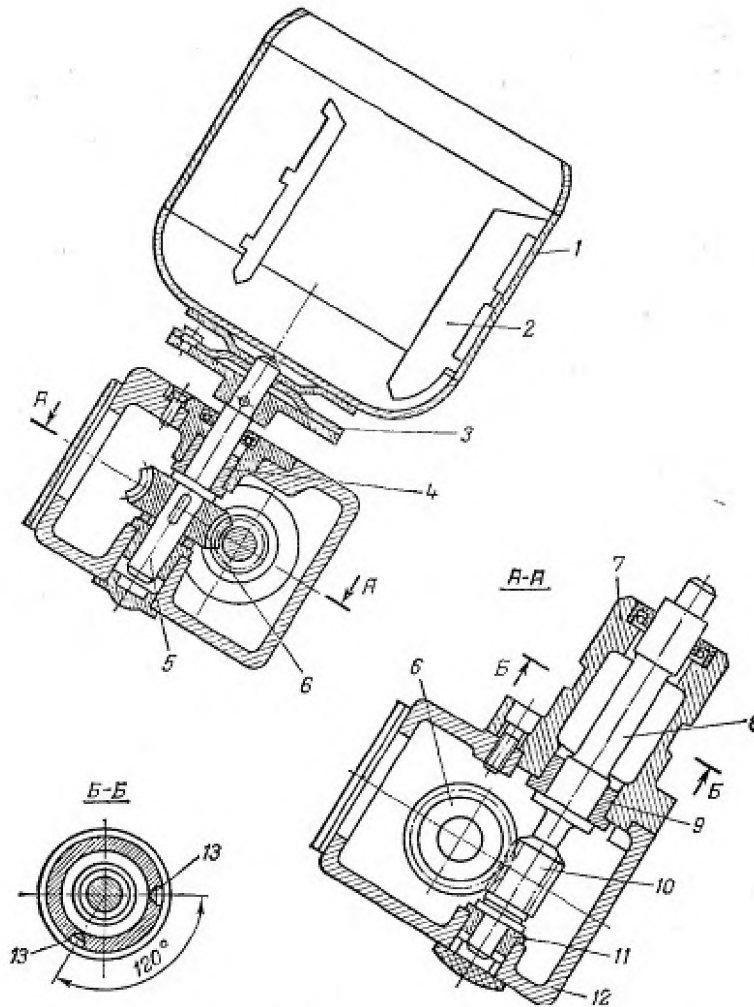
Механізм МС25-200 для перемішування овочів для салатів і вінегретів: 1 – бачок-барабан; 2 – ребра; 3 – фланець; 4 – втулки; 5 – вал; 6 – колесо черв'ячне; 7 – хвостовик; 8 – кільцева канавка; 9, 11 – втулки; 10 – черв'як; 12 – корпус редуктора; 13 – отвори, в які входять кінці гвинтів
